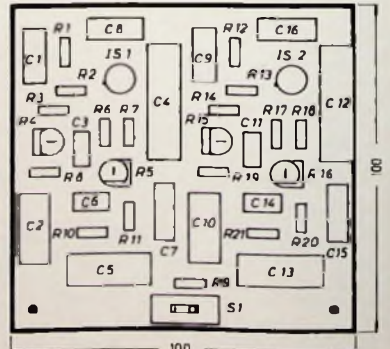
Aufbauplatine mit Lageplan der einzelnen Bauelemente
